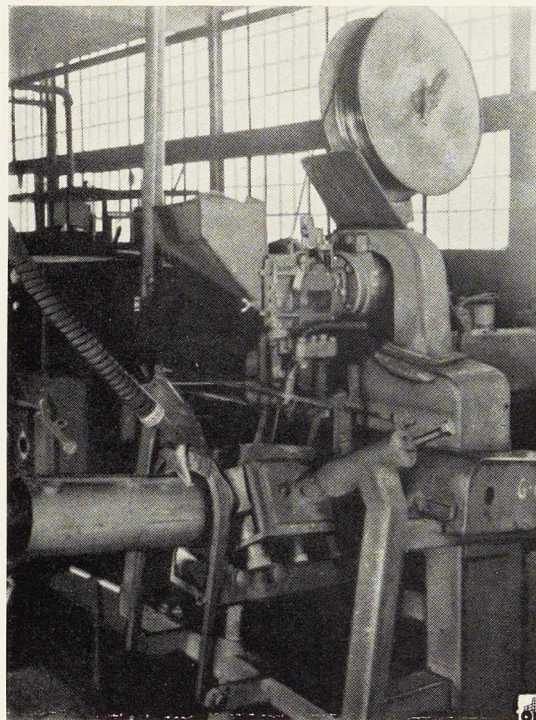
Machine pour le soudage des boîtes à obus de 1,5 mm d'épaisseur.
